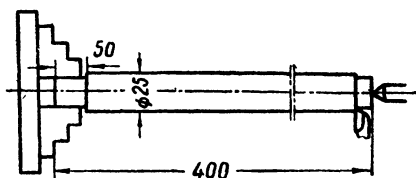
Крепление заготовки в патроне с поджатием задним центром.
